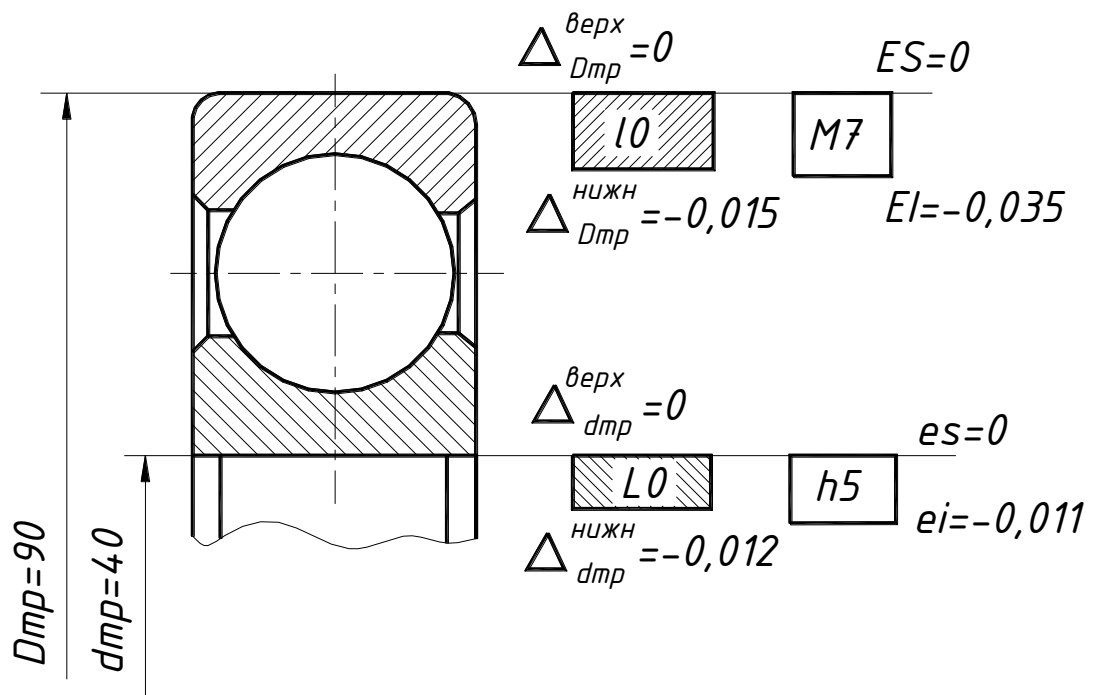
Схема розташування полів допусків кільця підшипника, вала і отвору в корпусі
